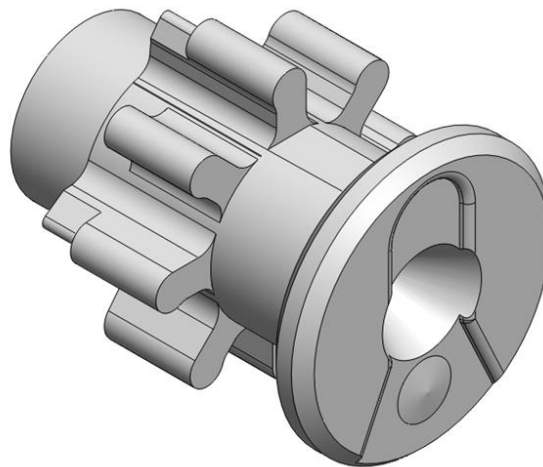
Modelo 3D de la pieza que conforma el engranaje de un sistema médico
